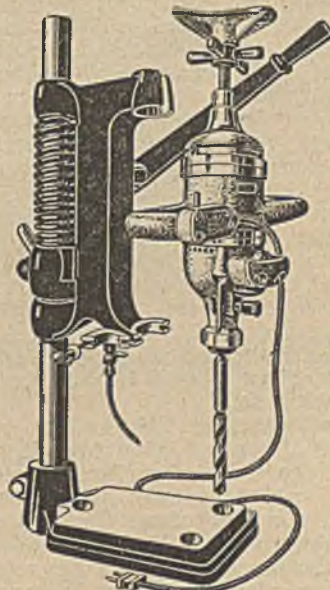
Elektrische Bohrmaschine der A. G. für Feinmechanik vorm. J. Petravice & Co.
